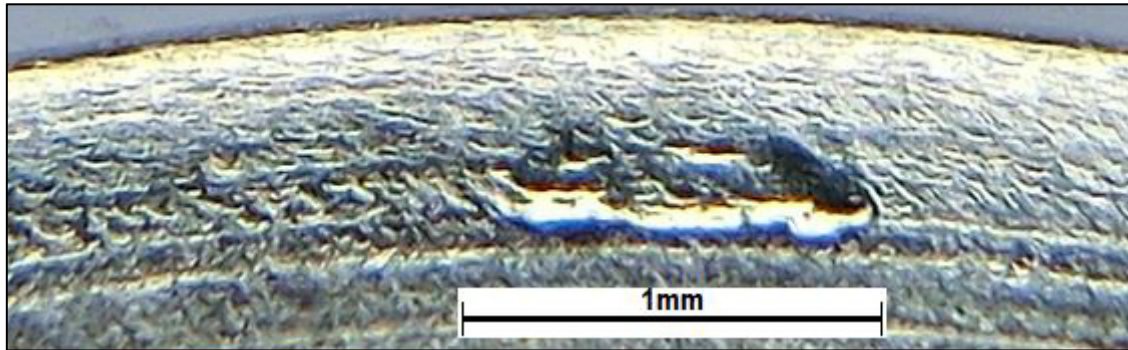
Sichtbarer zufälliger Oberflächenfehler auf einer Gewindeflanke
